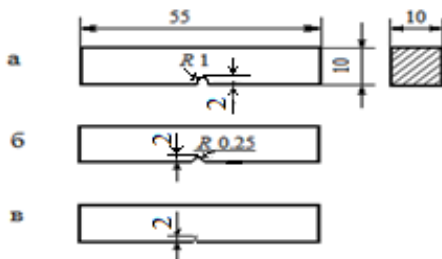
Образцы испытаний на ударную вязкость с различными концентраторами напряжений: а – U-образный; б – V-образный; в – T-образный с усталостной трещиной
